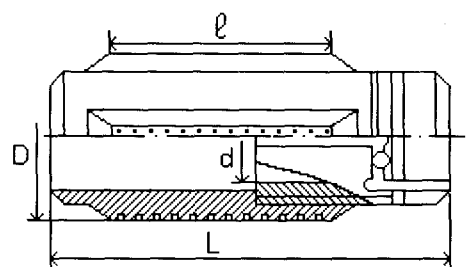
Передвижной центратор забойного двигателя 3-ЦДП
